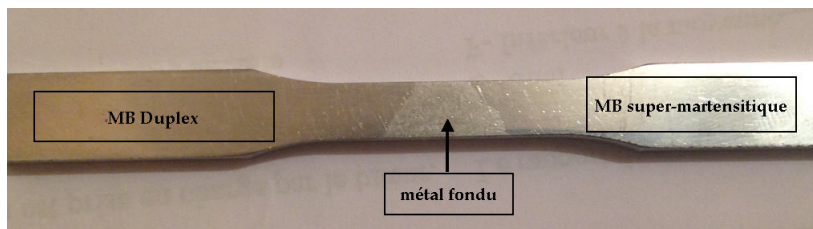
Présentation de l'éprouvette contenant une soudure au milieu.
